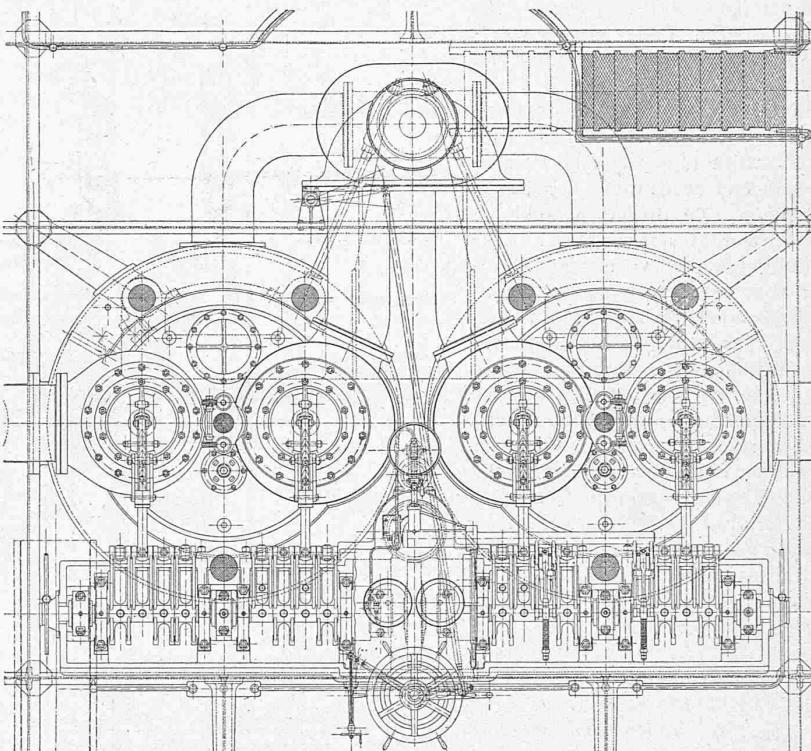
Grundriss (Schnitt zwischen den Cylindern) 1:50.
